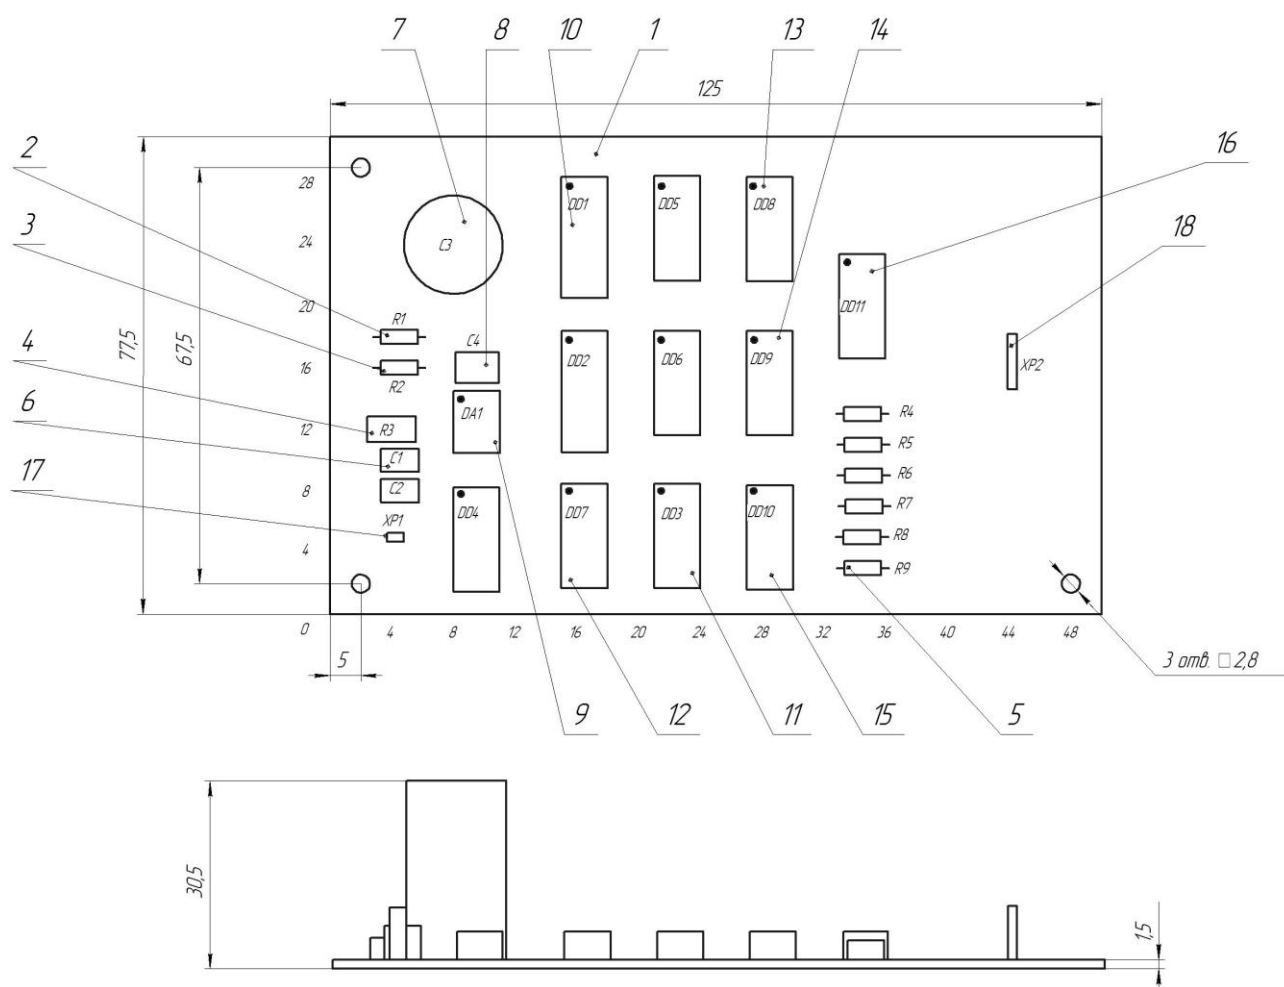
Фрагмент чертежа сборочного чертежа печатного узла системы
